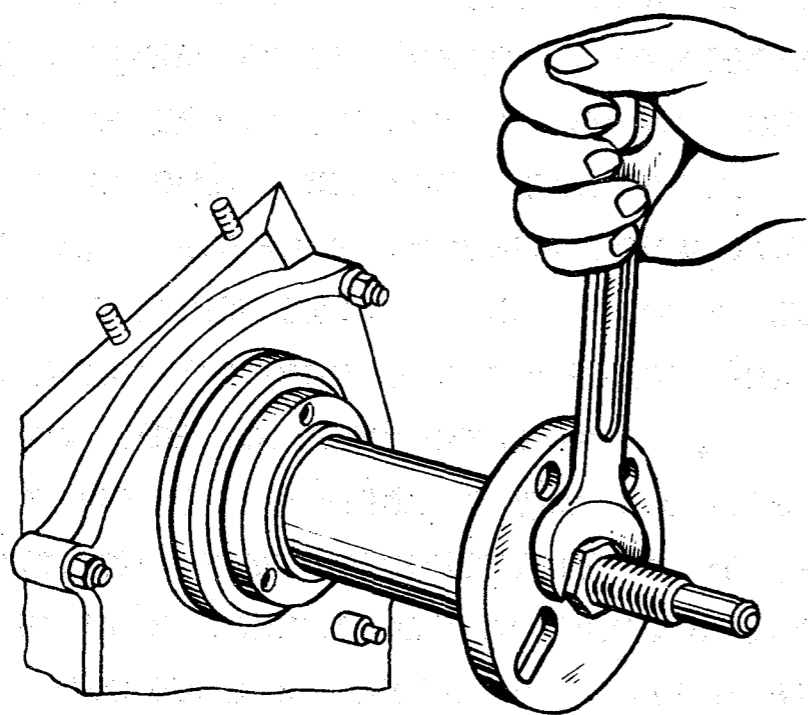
Напрессовка ступицы шкива коленчатого вала с помощью приспособления I6-Y-2368I7
